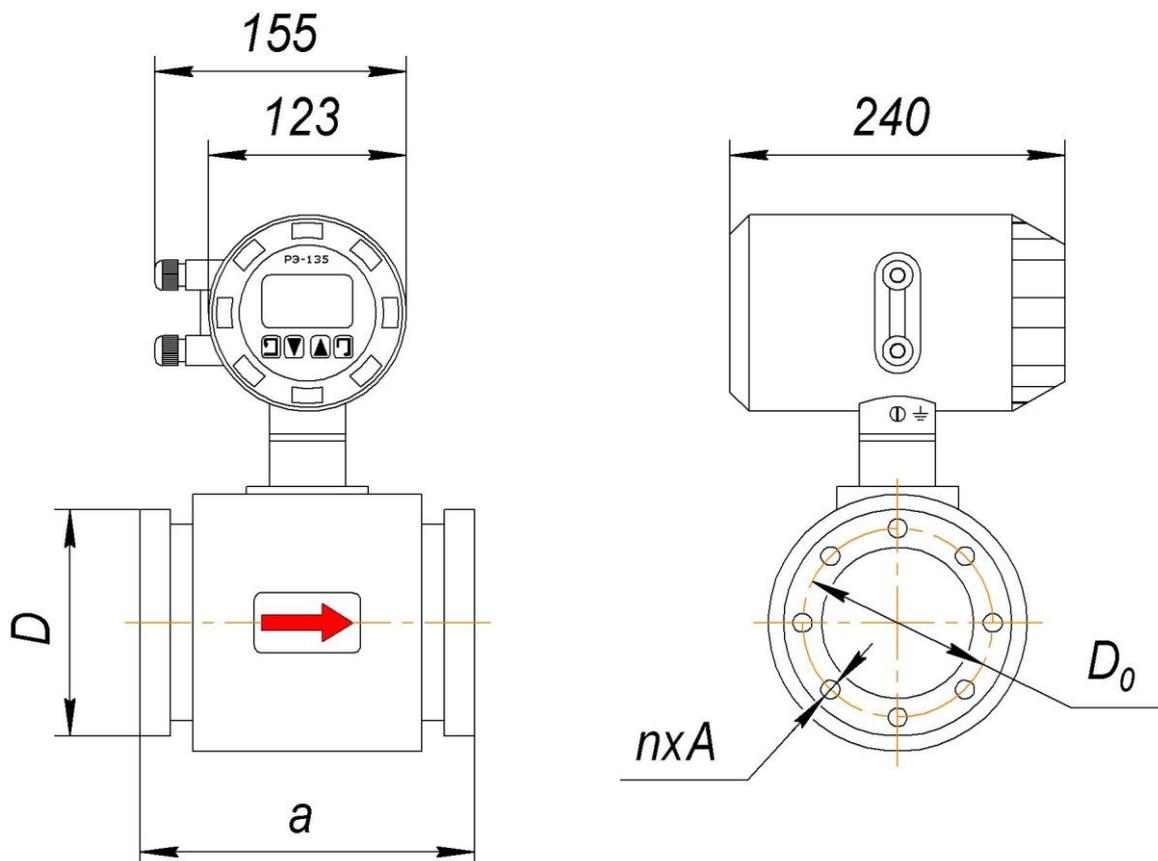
Габаритные и присоединительные размеры расходомера
